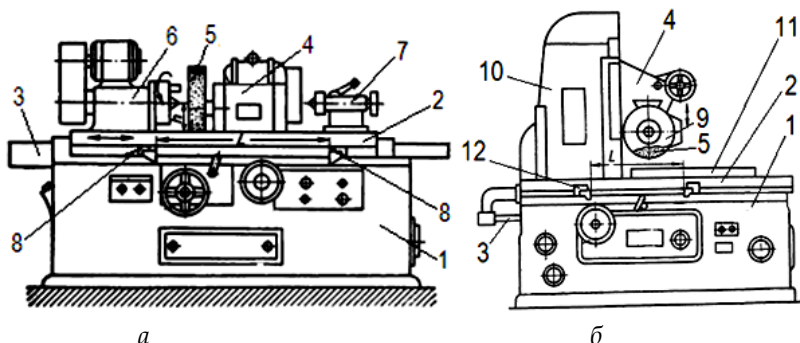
Кругло- (а) и плоскошлифовальный (б) станок:
